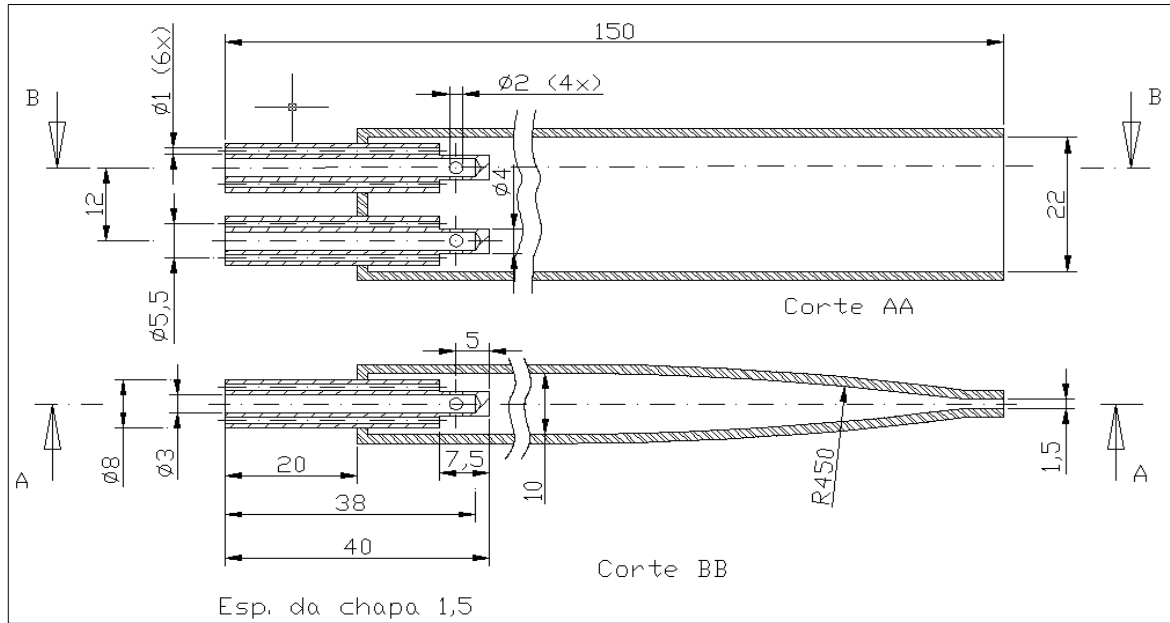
Desenho técnico em corte do bocal utilizado na técnica de aplicação do MQL.
